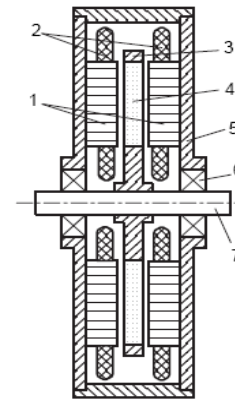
Descriptif de la machine à flux axial stator externe [GIE 06]
